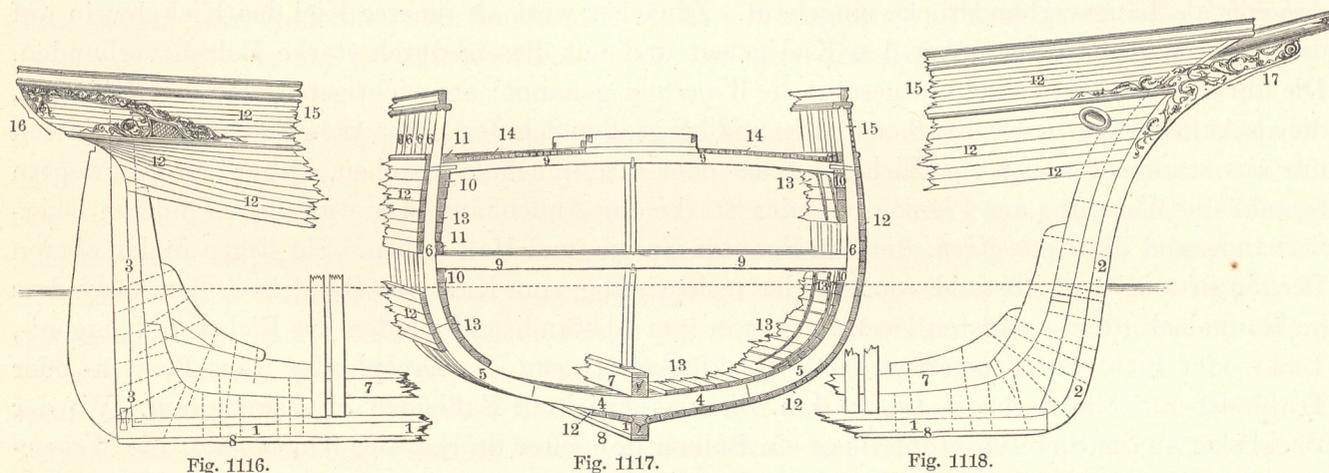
1118. Hölzernes Schiff (1 Kiel, 2 Vorsteven, 3 Achtersteven, 4 Bodenwrangen, 5 Kimmstücke, 6 Auflanger, 7 Kielschwein, 8 Loskiel, 9 Deckbalken, 10 Balkweger, 11 Wassergänge, 12 äußere Beplankung, 13 innere Beplankung, 14 Oberdeckbeplankung, 15 Reling, 16 Heck, 17 Galion).
